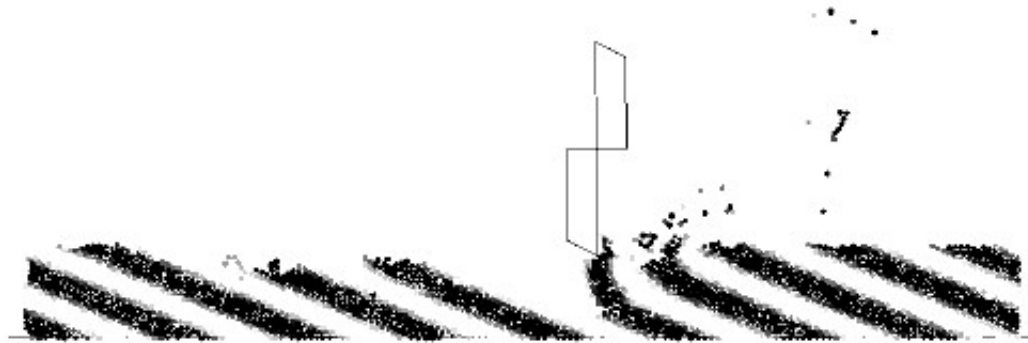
Моделювання процесу фрезерування деревини
